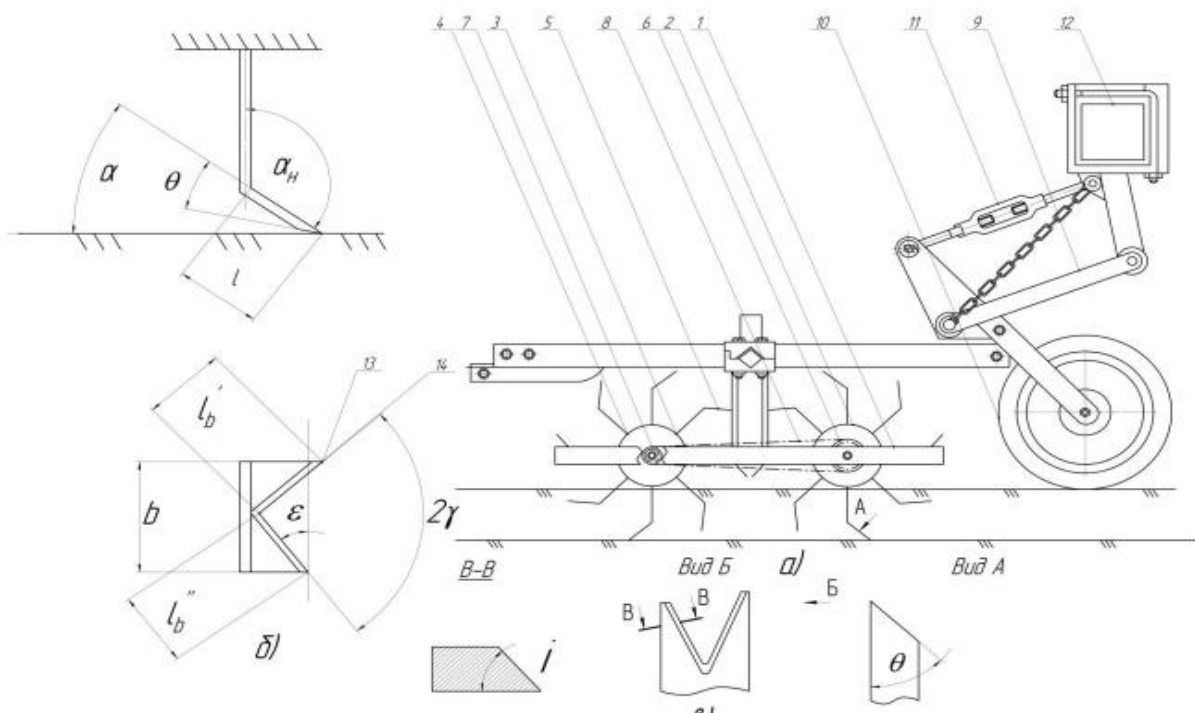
Секційний робочий орган: а) загальний вигляд; б) схема ножа ротора; в) схема вирізу ножа ротора; 1 – корпус; 2 – передній ротор; 3 – задній ротор; 4 – диск; 5 – ніж; 6 – зірочка переднього ротора; 7 – зірочка заднього ротора; 8 – ланцюгова передача; 9 – паралелограмний механізм; 10 – опорне колесо; 11 – гвинтова стяжка; 12 – брус; 13 – передня кромка ножа; 14 – виріз леза ножа.
